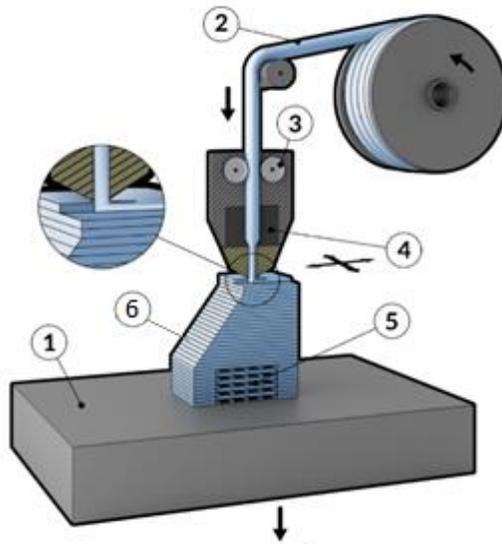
Modelado por deposición fundida. 1) mesa de impresión 2) filamento plástico 3) rodillos impulsores del material de manufactura 4) extrusor 5) material de soporte 6) pieza manufacturada.
